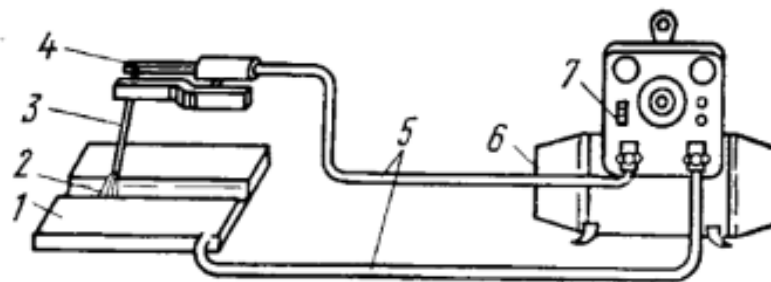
Вигляд поста для ручного дугового зварювання
